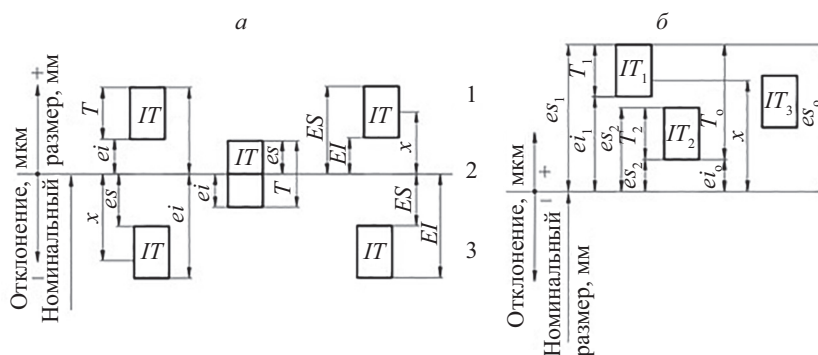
Схемы расположения допуска (а) и верхних пределов качества (б)
